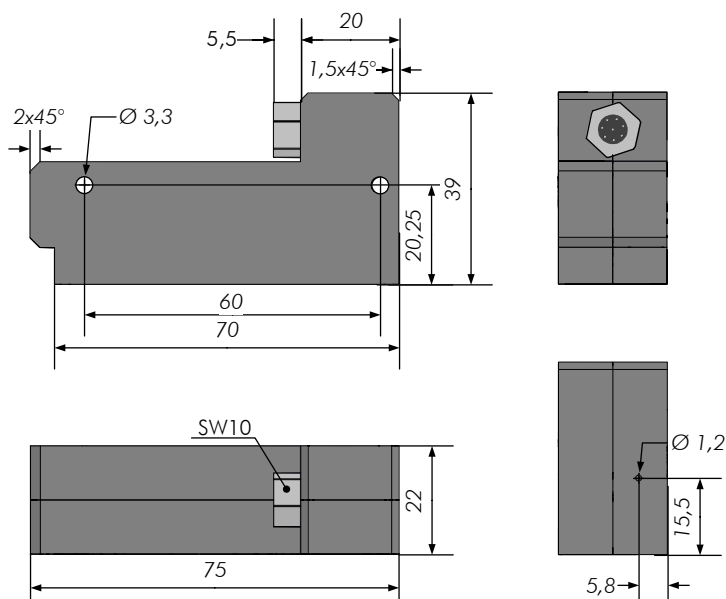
Abmessungen Sensor mit M9-Rundstecker
